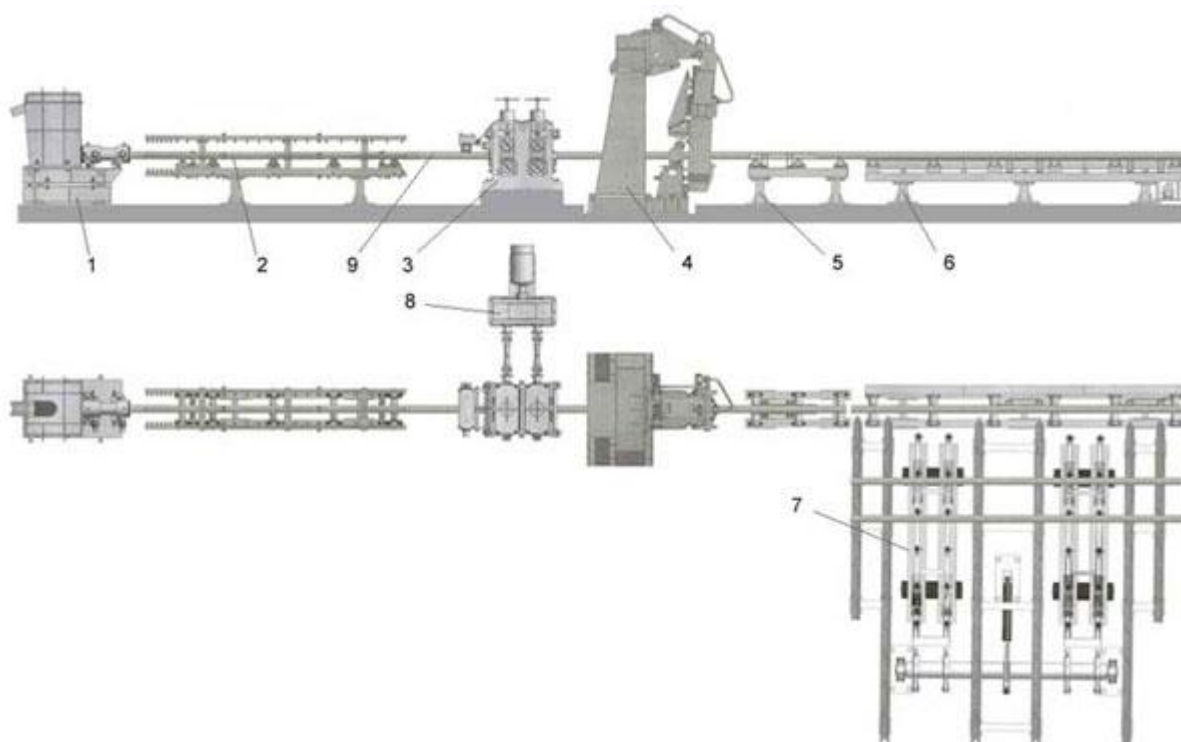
Устройство горизонтальной машины непрерывного литья заготовок
